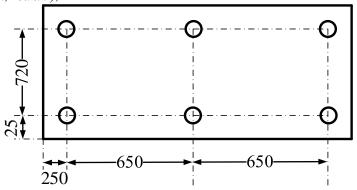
Схема крепления виброизоляторов (вид сверху)
